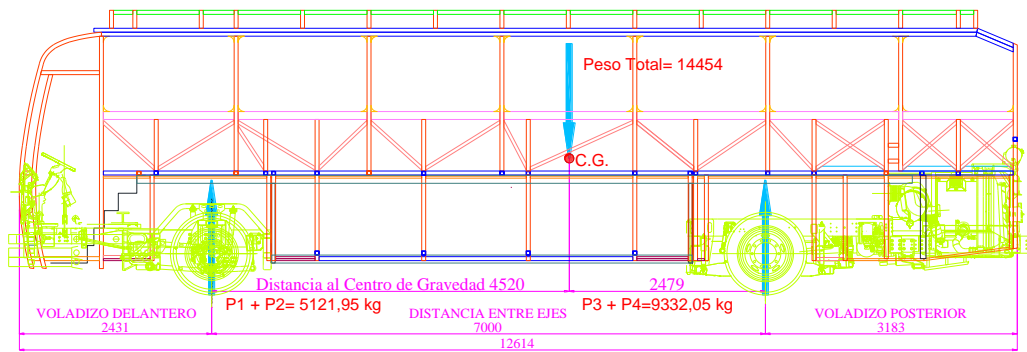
Distribución de secciones y pórticos de la superestructura propuesta.
